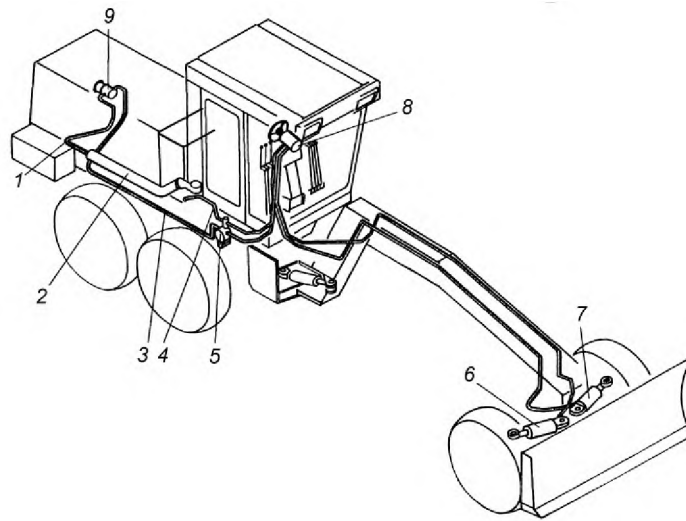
Рулевое управление автогрейдера А120: 1 – рукав всасывания; 2 – заборная труба; 3 – напорная гидрелиния; 4 – рукав слива; 5 – предохранительный клапан; 6, 7 – гидроцилиндры; 8 – гидроруль; 9 – насос
